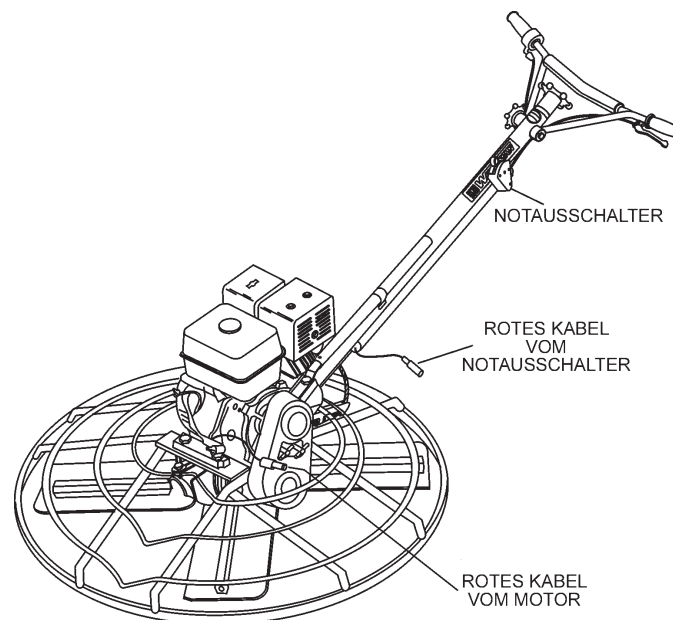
Kabelverbindung für Notauschalter des Motors
